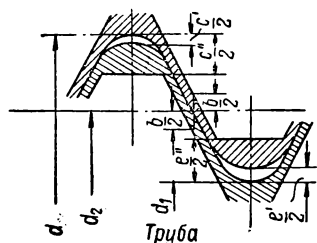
Схема расположения полей допусков трубной резьбы.
